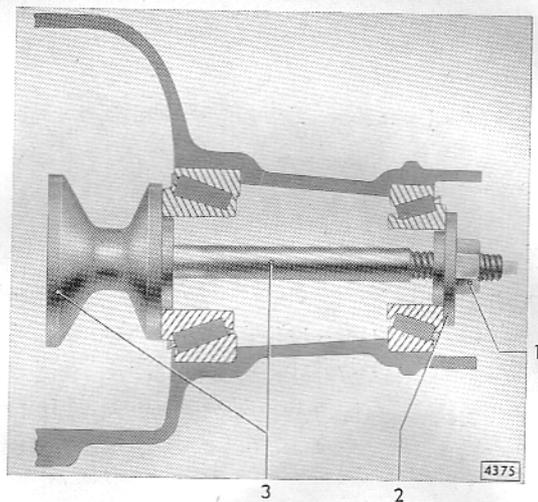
Meßplatte des Antriebskegelrad-Einstellwerkzeuges S-5001 im Achsgehäuse eingebaut
